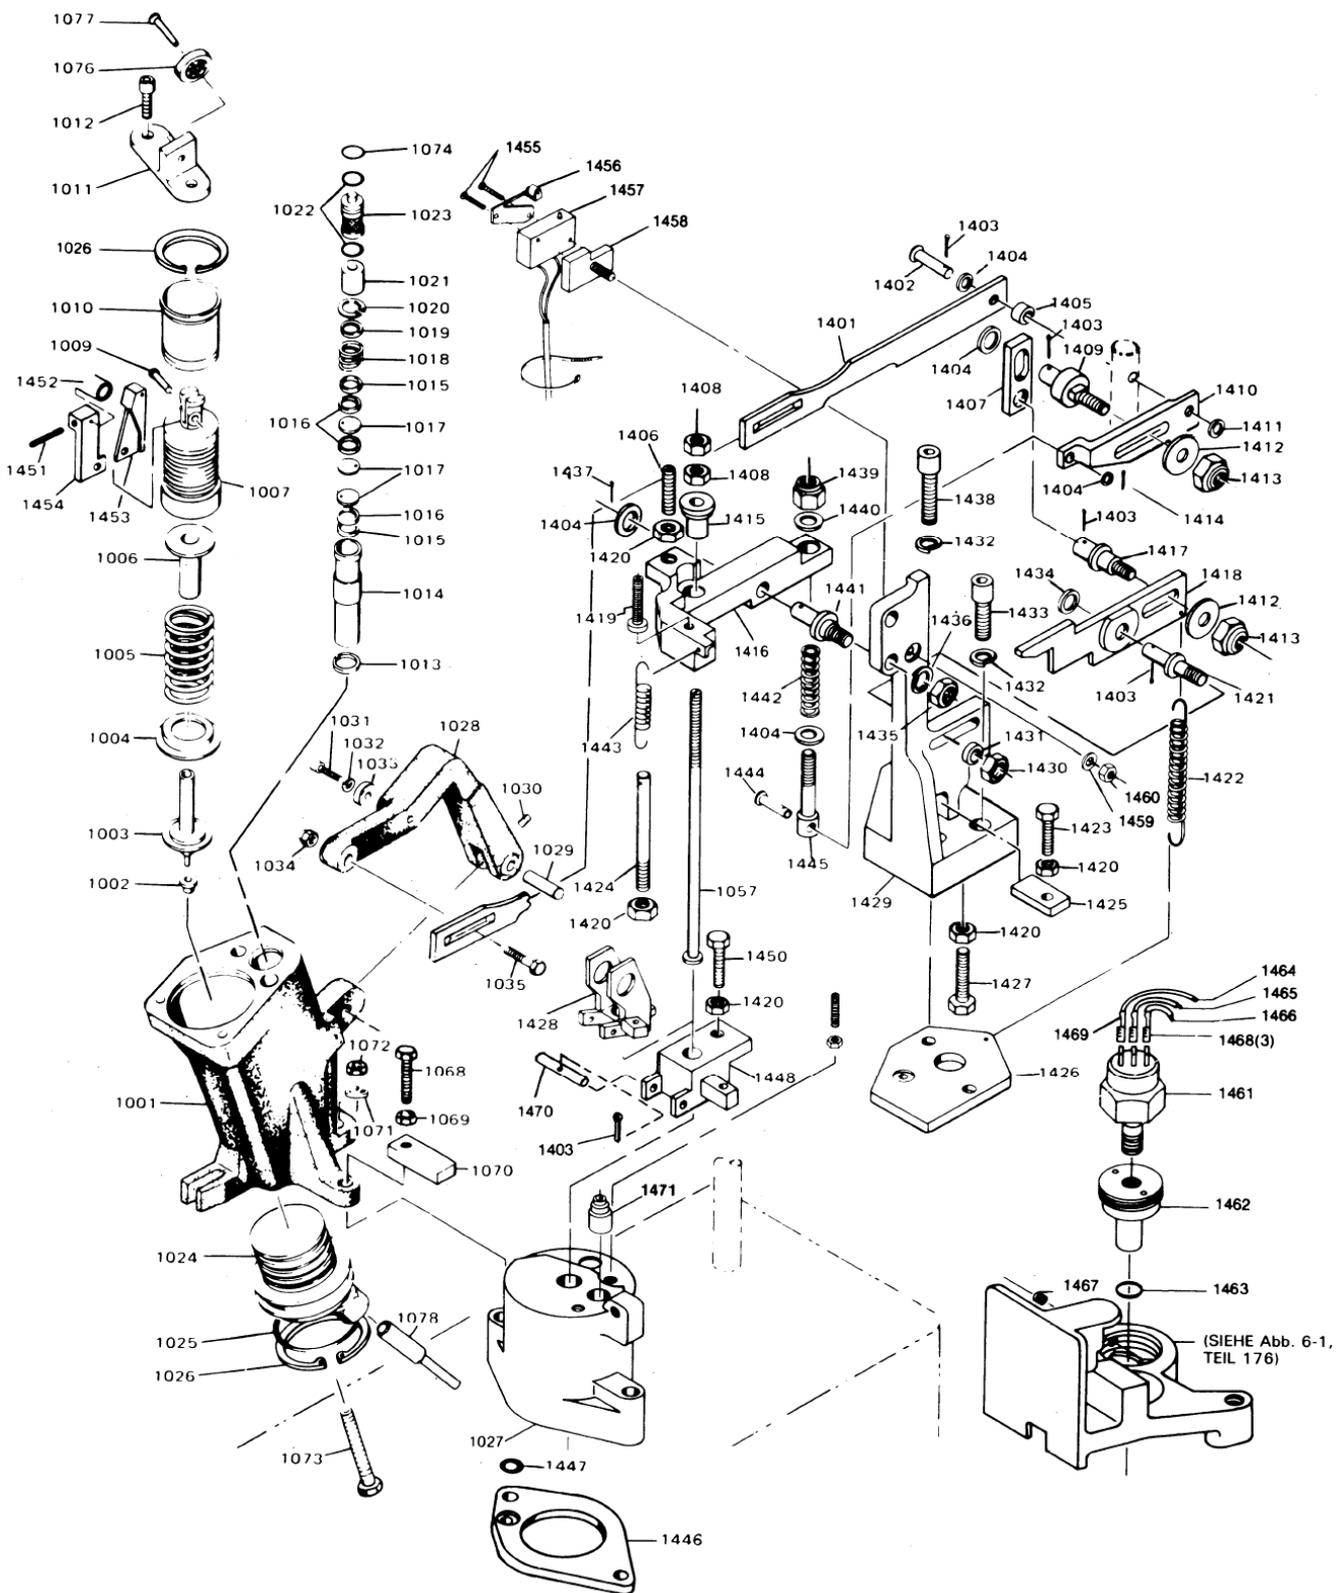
Explosionsdarstellung der drehzahlwert- und des 'schrägen' aufladedruckabhängigen Füllbegrenzers mit Druck und Microschalter
